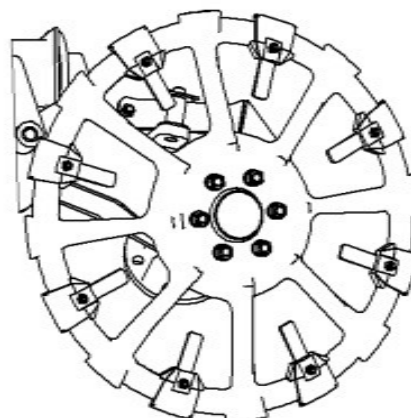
Колесо подъемника 69855 с Rim Mounted Filler Tabs. Примечание: Центр монтировать колеса наполнители также доступны на этом колесе подъемника.
